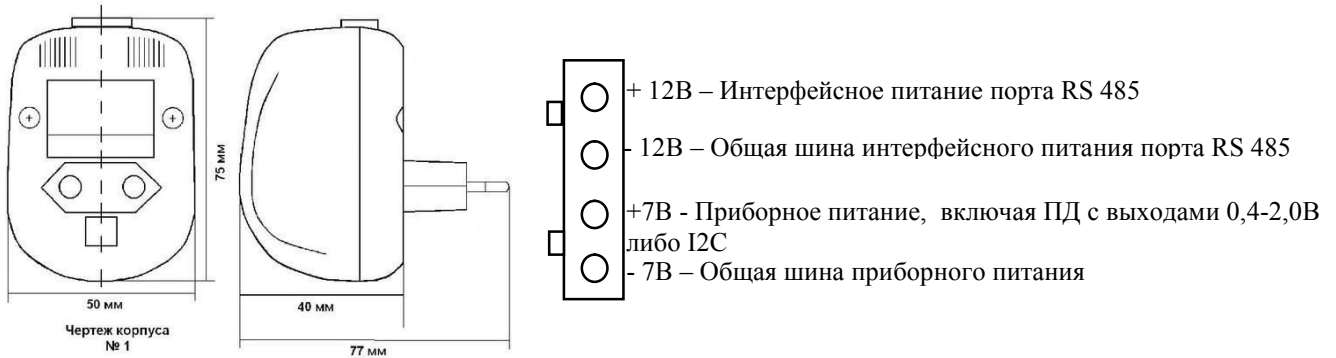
Размеры корпуса источника питания БП-5.
